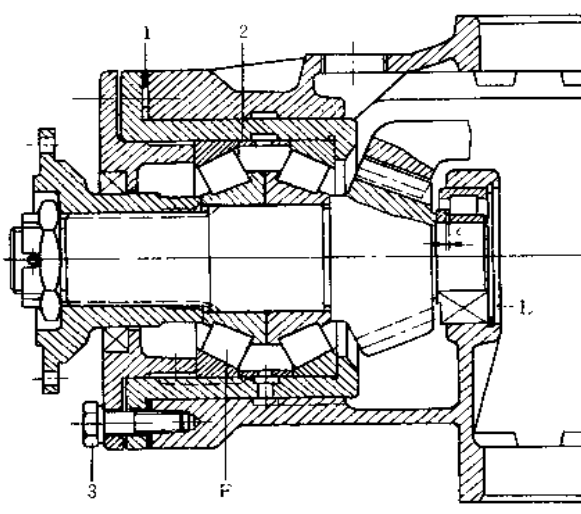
成对圆锥滚子轴承和圆柱滚子轴承的轴向固定
